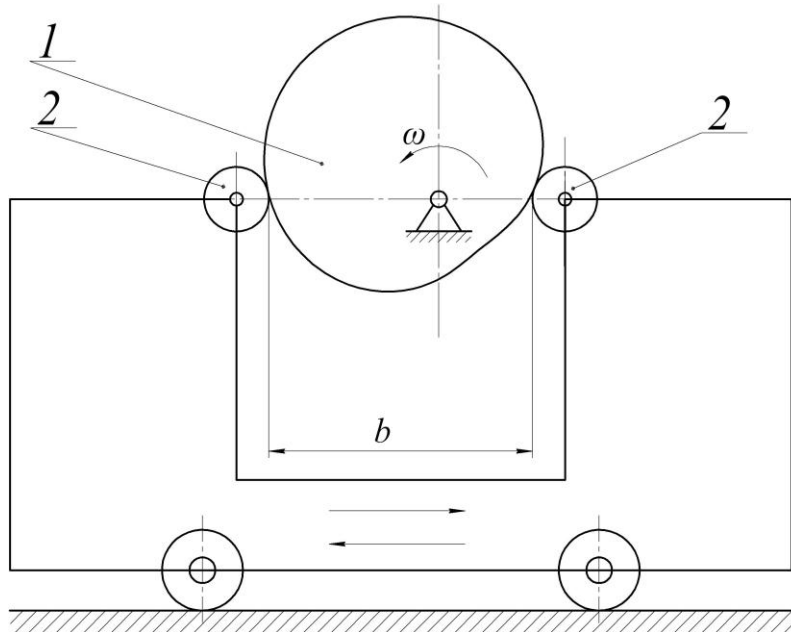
Схема механізму з кулачковим приводом зворотно-поступального руху візка
